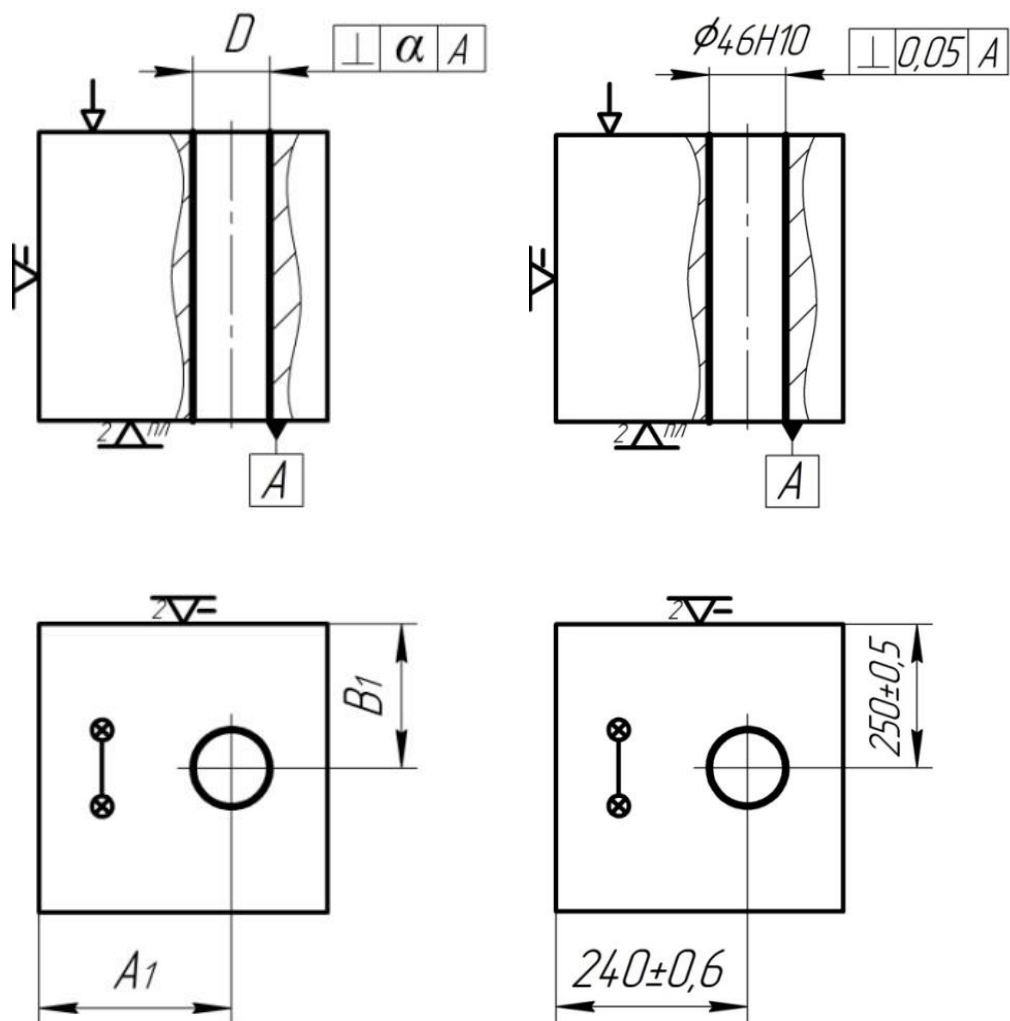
Схема установки и операционный эскиз для обработки рассматриваемой заготовки
